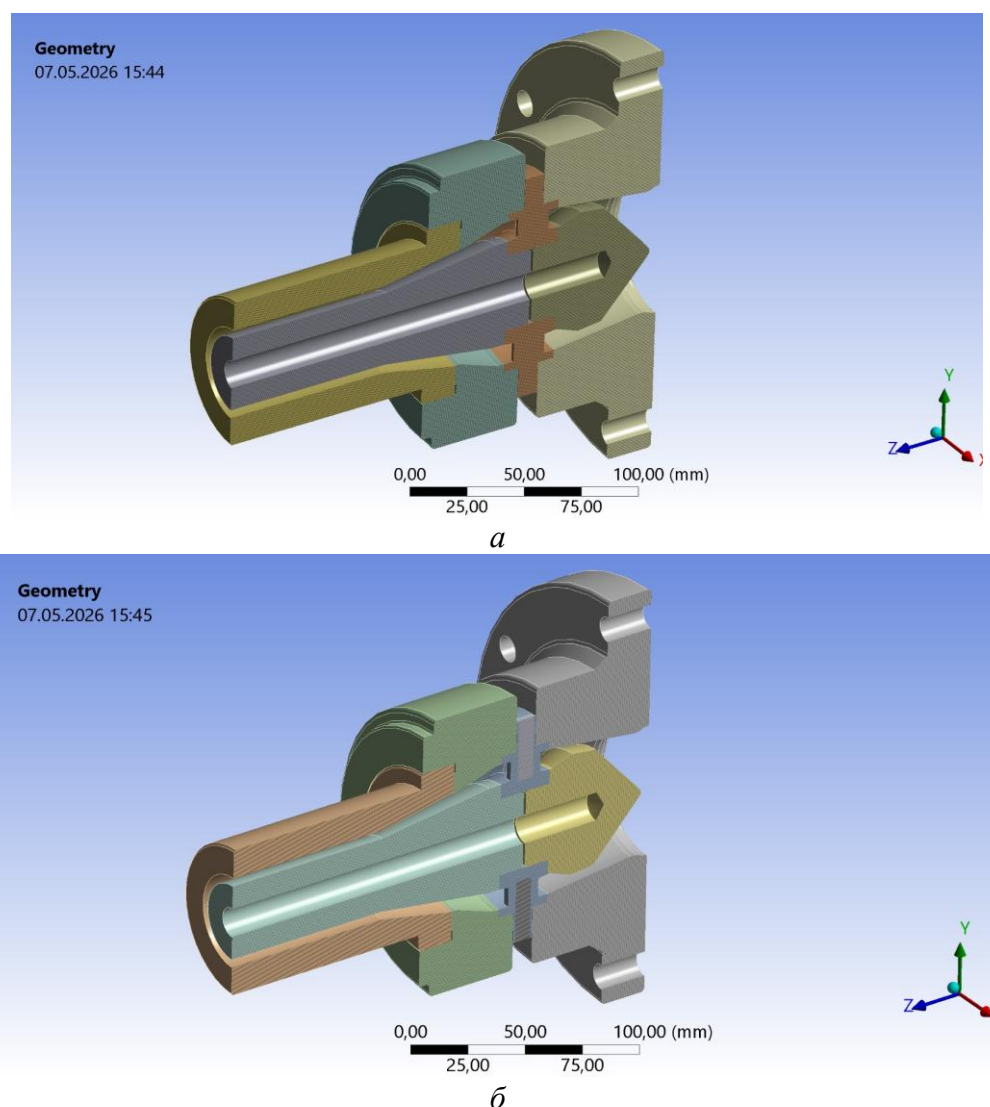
3D-модель формуючої головки у розрізі: а – базова; б – модернізована
